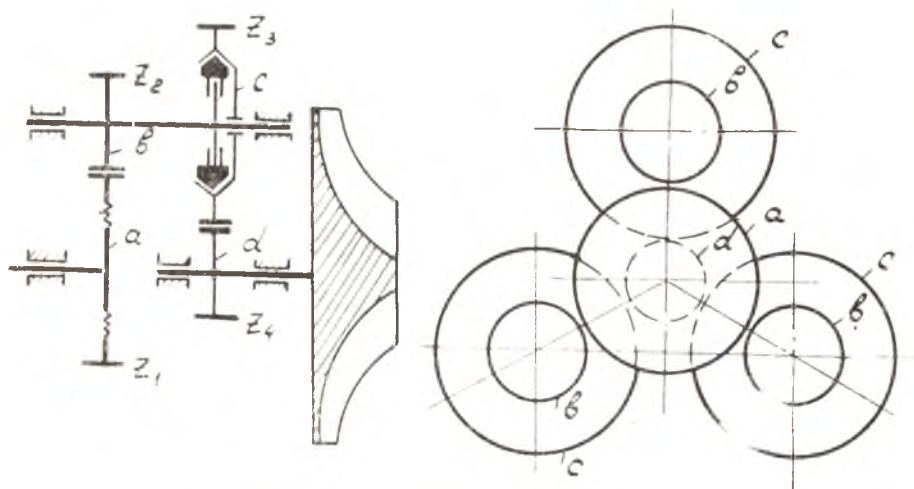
1. Конструкция узла компрессора центробежного типа.
